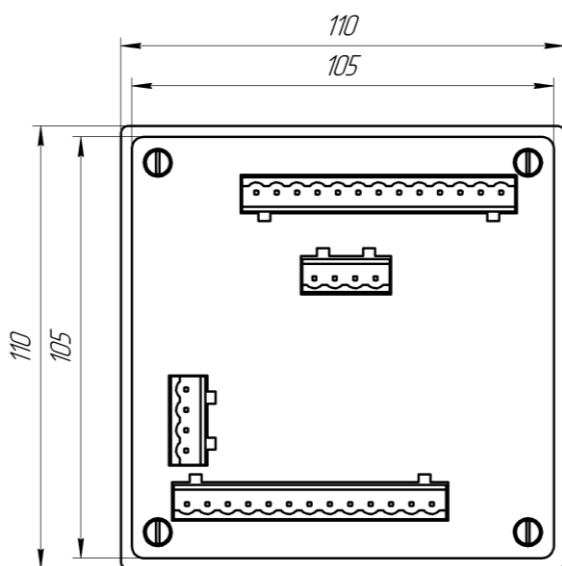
Габаритный чертеж измерителя MI-xAC (вид сзади)
